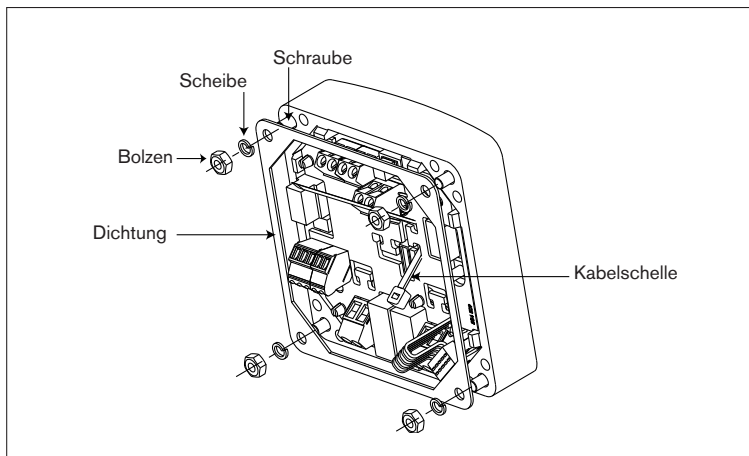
Installation Redox-Transmitter 8206, Schaltschrank-Ausführung
